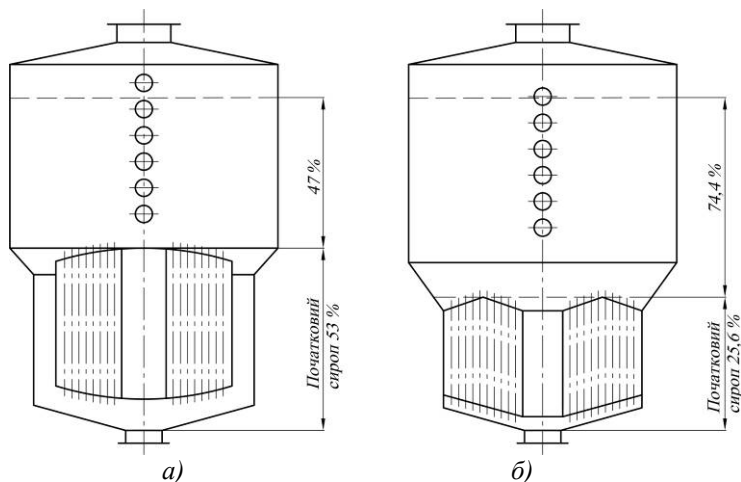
Схеми конструкцій вакуум-апаратів: а) ВМА-600; б) ВАМЦ-600.
